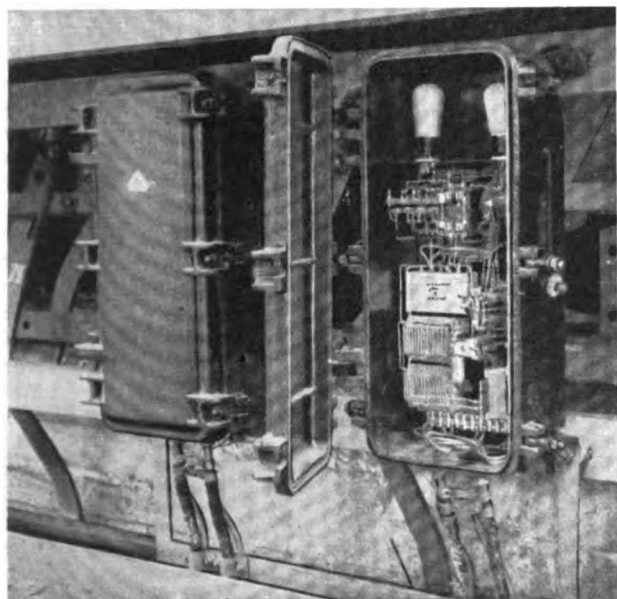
Anbau der Verstärker zur lichtelektrischen Scherensteuerung an dem Kühlbett einer Walzenstraße.
